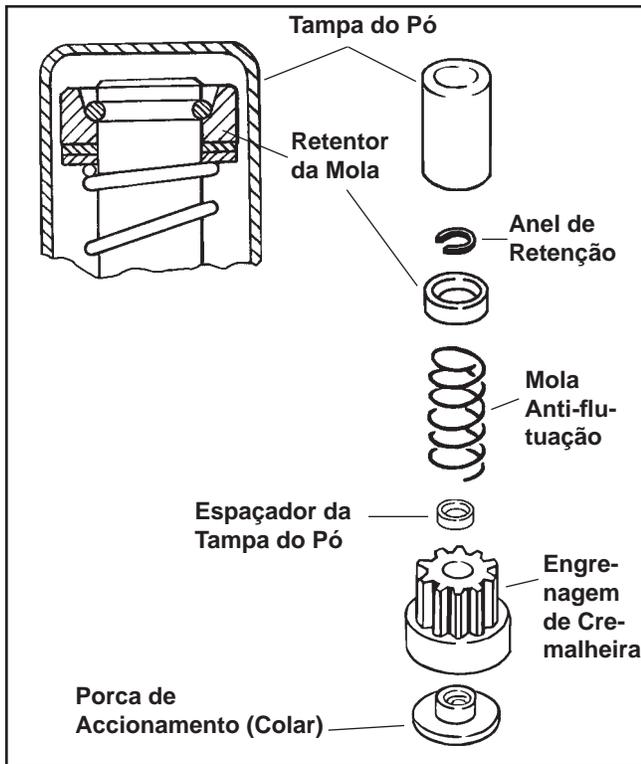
Componentes do Accionamento, Motor de Arranque de Accionamento por Inércia “Soldado”.
